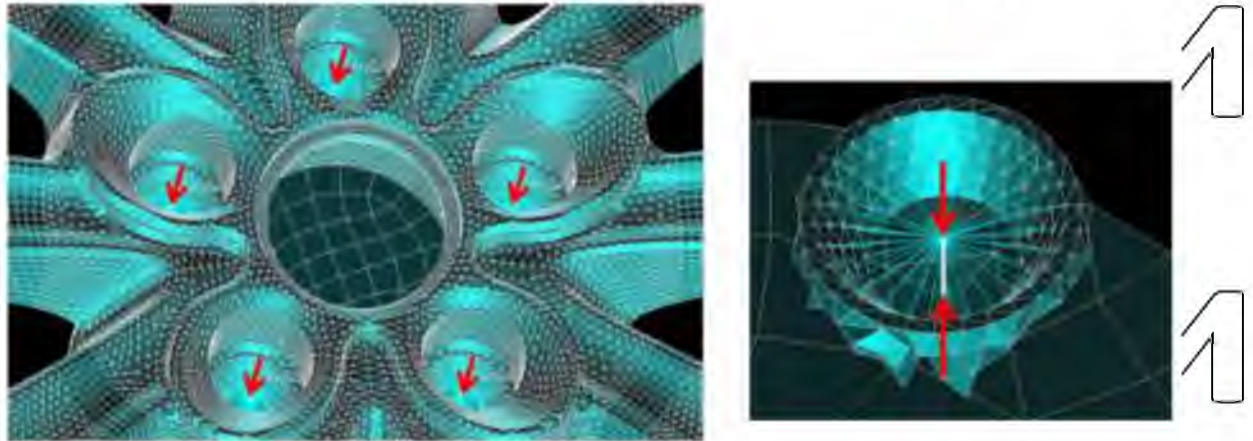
Особливості розрахункової схеми обліку роботи болтового з'єднання литого колеса з маточкою
